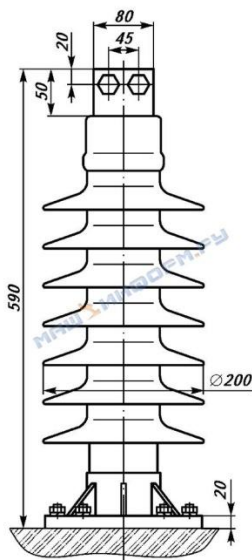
Общий вид и габаритные размеры ОПН-П1-10/12,7/10/3 УХЛ1
